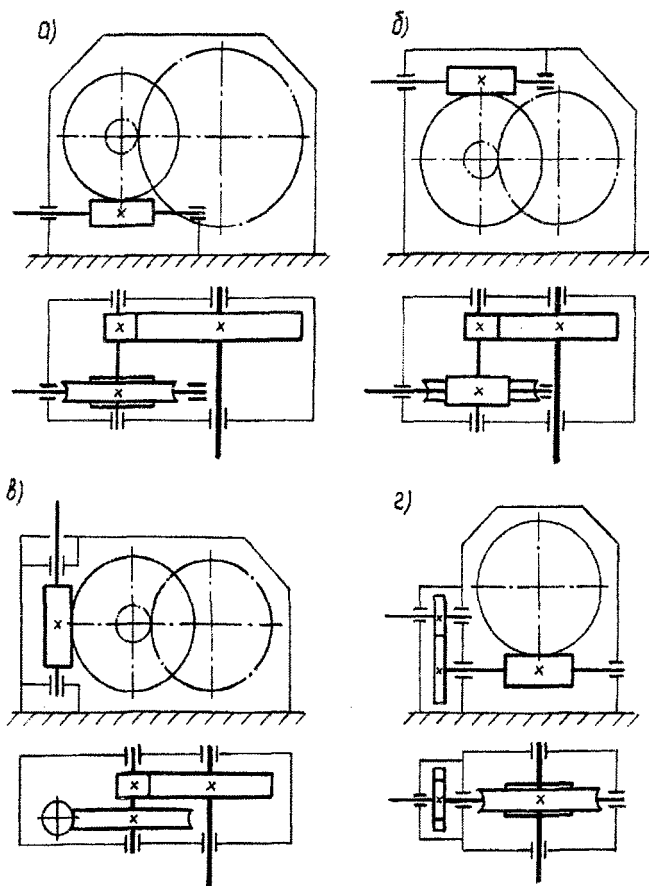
Схемы комбинированных редукторов на базе червячной передачи
